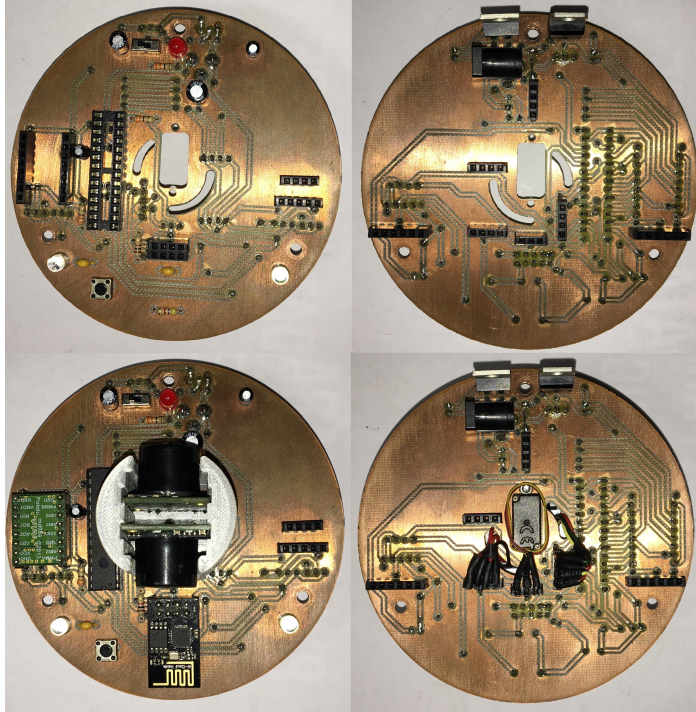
Arriba a la izquierda, vista superior de la placa con componentes soldados. Arriba la derecha, vista inferior. Abajo a la izquierda, vista superior de la placa con módulos, servomotor y ultrasónicos incorporados. Abajo a la derecha, vista inferior con las incorporaciones.
